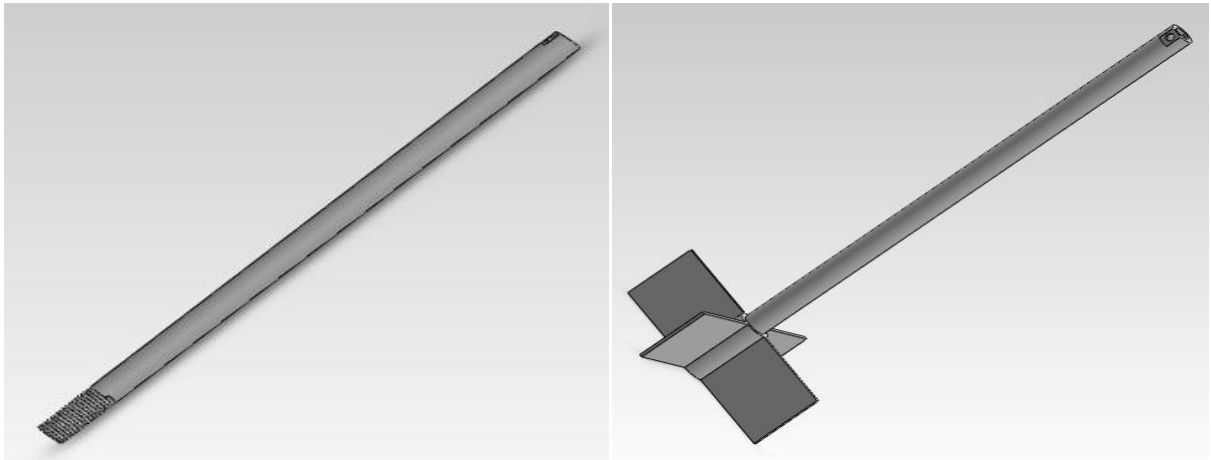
material part 3 setelah dilakukan pengelasan pada tutup dan dudukan motor pengaduk
